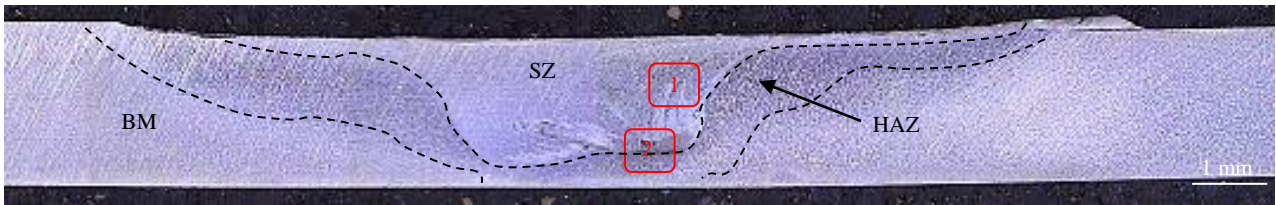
焊接 180 mm 后焊缝横截面的宏观形貌
